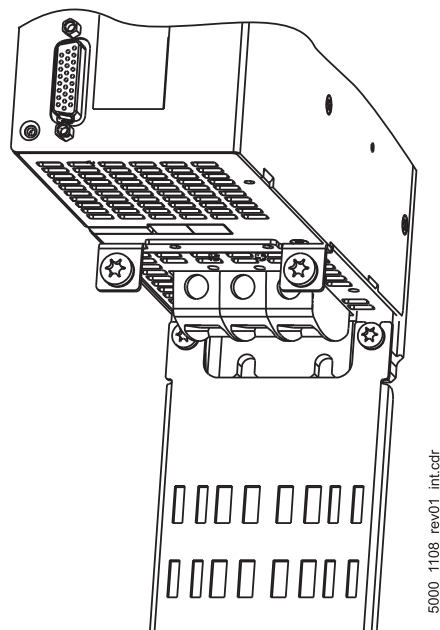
Montage Schirmblech Cold Plate Geräte
